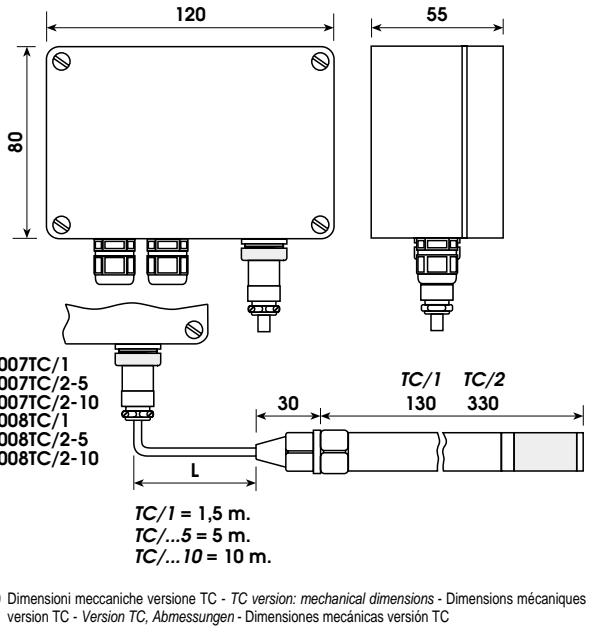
Dimensioni meccaniche versione TC - TC version: mechanical dimensions - Dimensions mécaniques version TC - Version TC, Abmessungen - Dimensiones mecánicas versión TC
